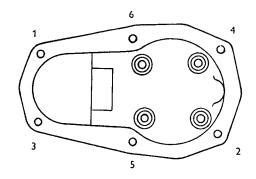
Ordre de serrage des vis du couvercle de l'allumeur.
